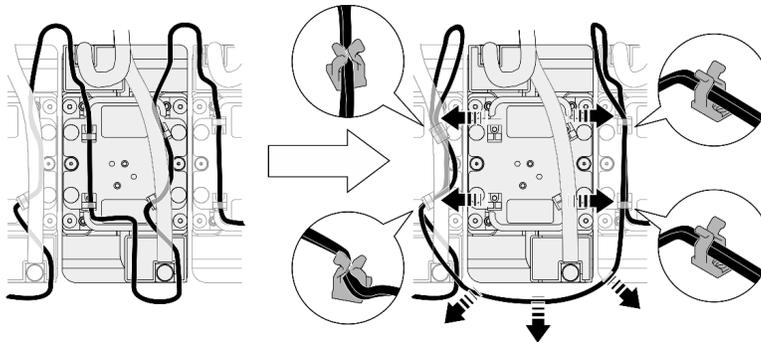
Removendo os cabos do módulo do sensor de vazamento
